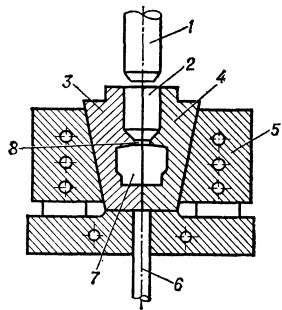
Схема установки для литьевого прессования на универсальном прессе: 1 — поршень; 2 — камера; 3—4 — полуматрицы; 5 — обойма; 6 — выталкиватель; 7 — оформляющее гнездо прессформы; 8 — литниковый канал.
